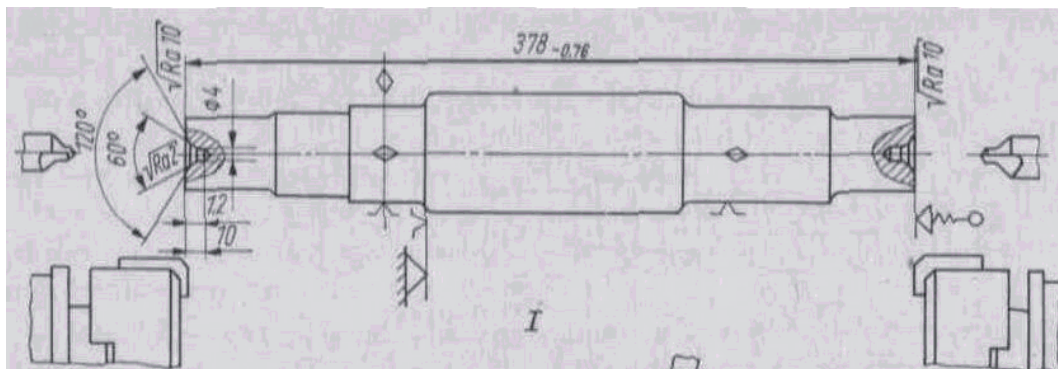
Комбинированная параллельно-последовательная обработка вала на фрезерно-центровальном станке
